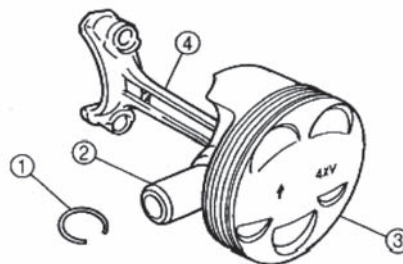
Pohled do vnitřku motoru BMW K 100.
